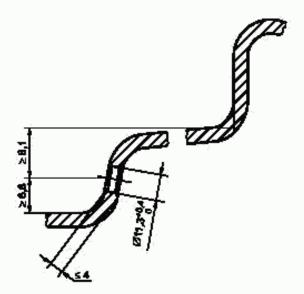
Размеры вентильного отверстия для бескамерных шин
